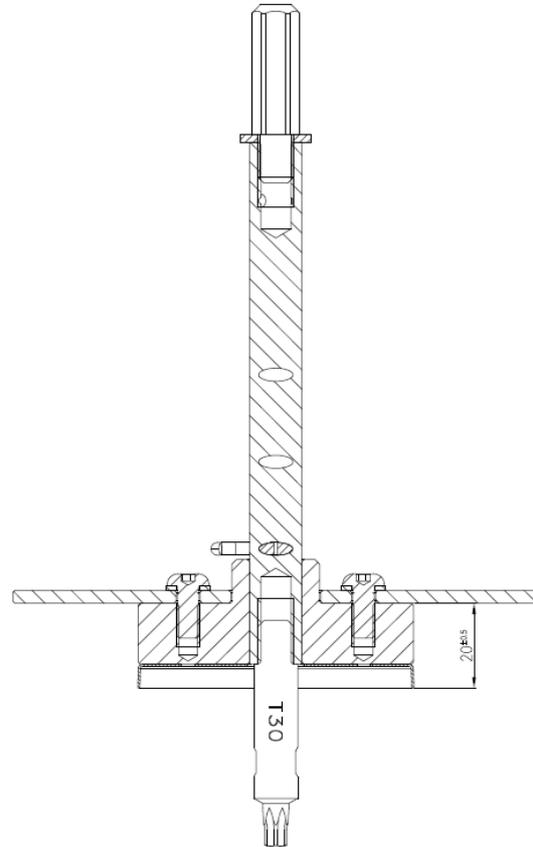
ejotherm STR U 2G Montagewerkzeug Typ "S"
